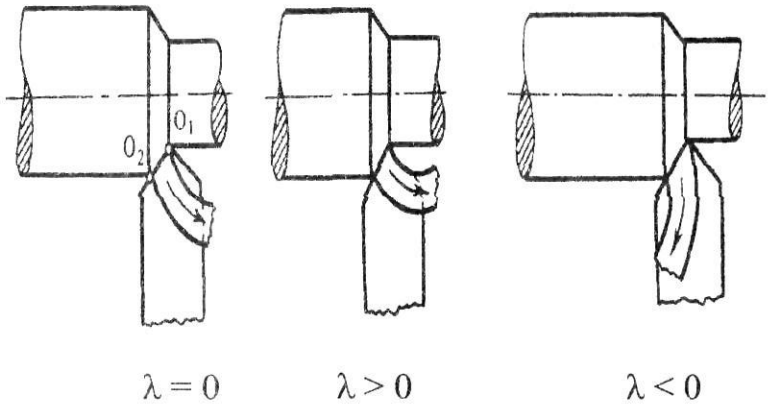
Влияние угла наклона главной режущей кромки « λ » на направление движения схода стружки
